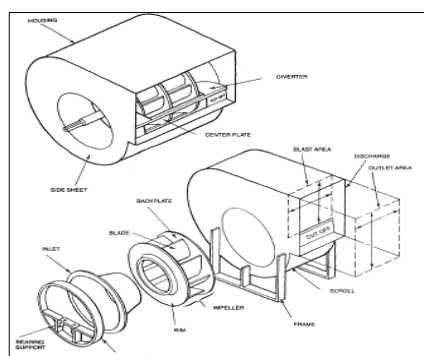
PARTES DE UN VENTILADOR CENTRÍFUGO
